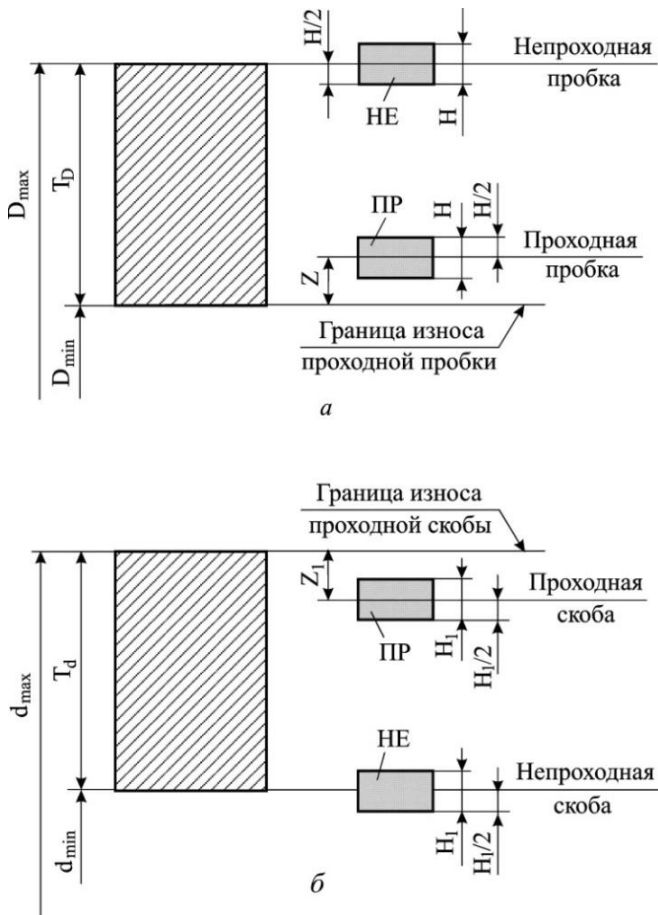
Схемы расположения интервалов допусков гладких калибров для контроля отверстий (а) и валов (б) с номинальными размерами до ISO мм и допуском изготовления по IT6-IT8
